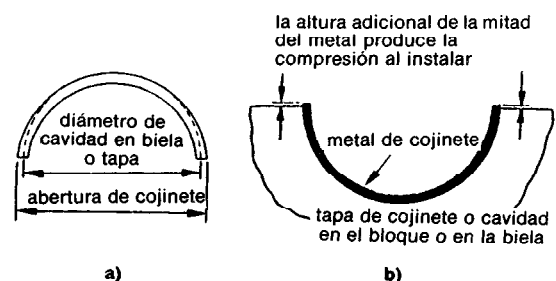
a) Abertura de cojinete, b) Compresión del metal
